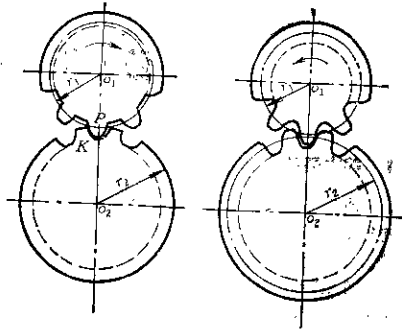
单圆弧齿轮传动和双圆弧齿轮传动
